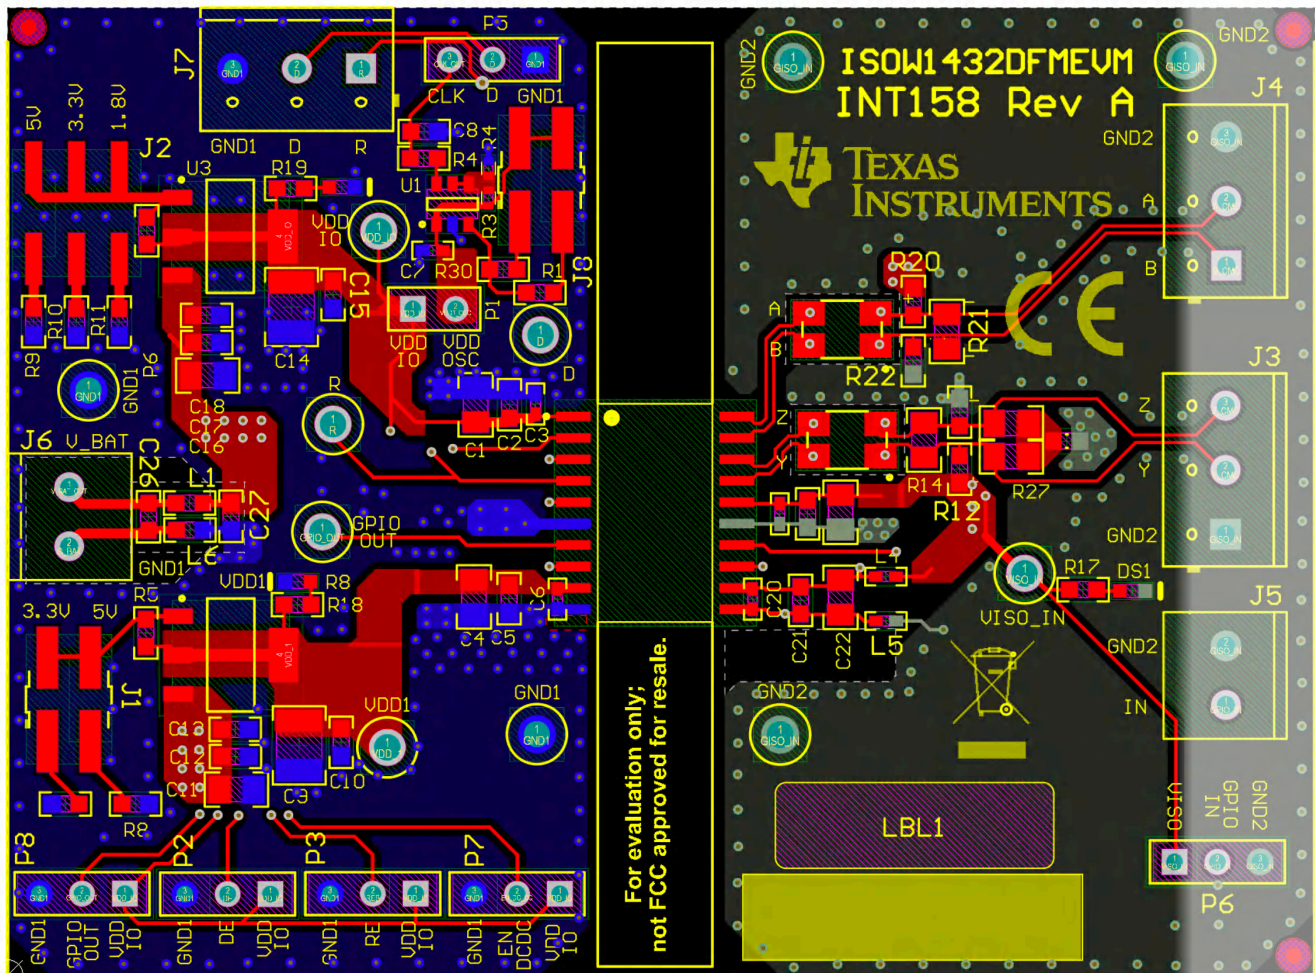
ISOW1432DFMEVM PCB 布局 - 顶层
